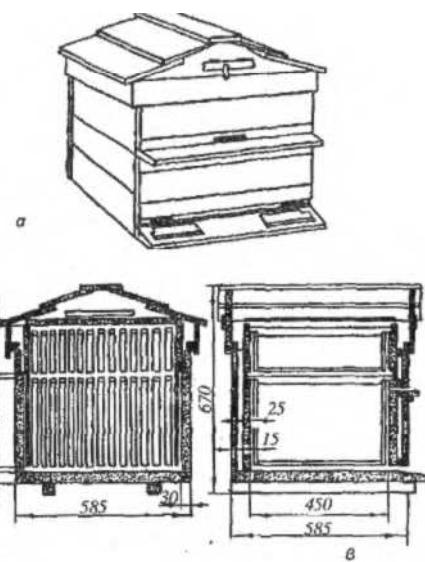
Утепленный 14-рамочный улей: а — общий вид; б, в — его устройство (продольный и поперечные разрезы)
